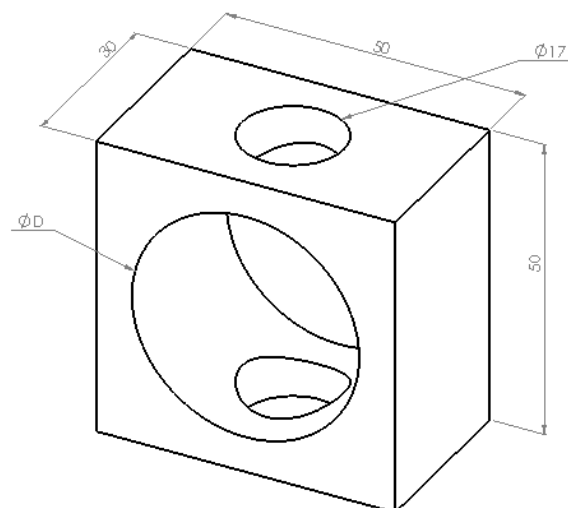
Dimensões do sensor paralelepípedo (mm).
